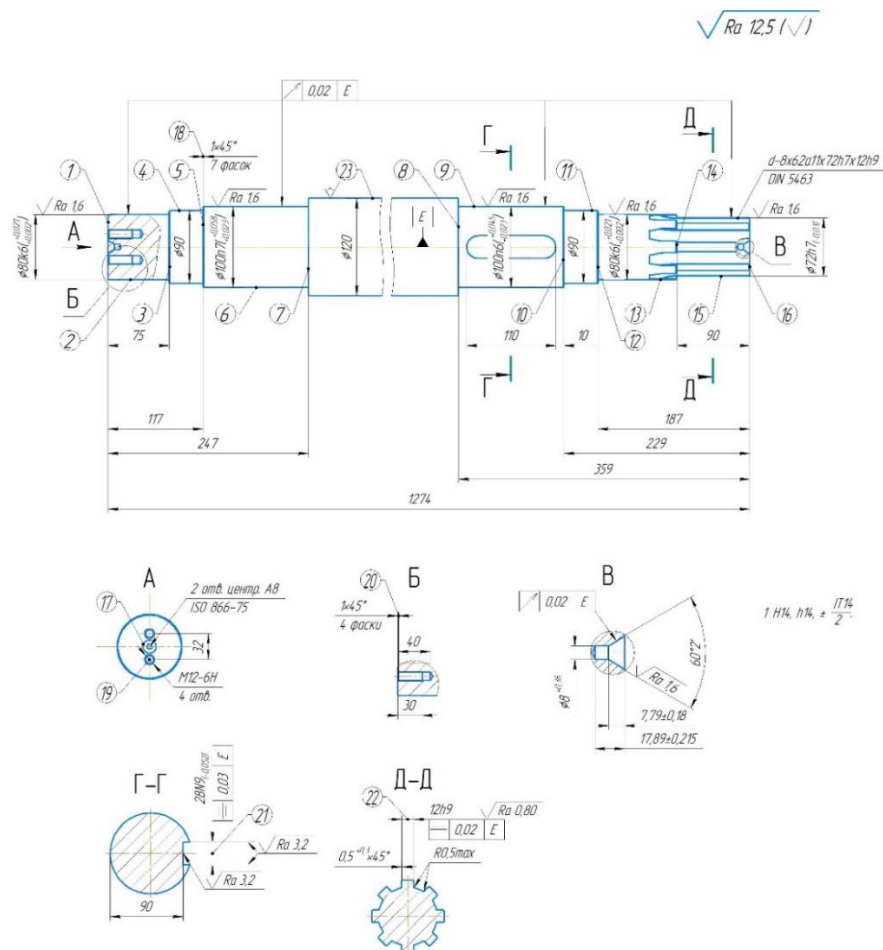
Поверхні деталі «Вал» привідного барабану
